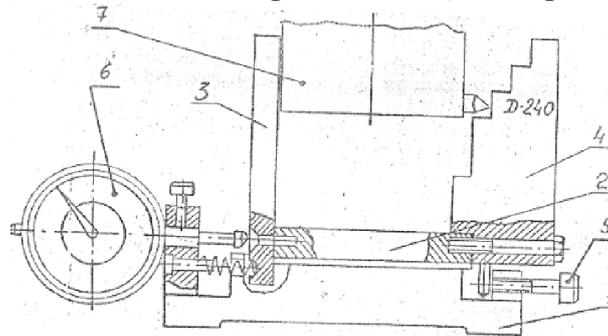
Приспособление для установки вылета резца на необходимый диаметр растачиваемого отверстия: 1 – основание с направляющими; 2 – каретка; 3 – передняя планка; 4 – задняя ступенчатая упорная планка; 5 – винт настроечный; 6 – индикатор часового типа; 7 – резцовая головка шпинделя станка
